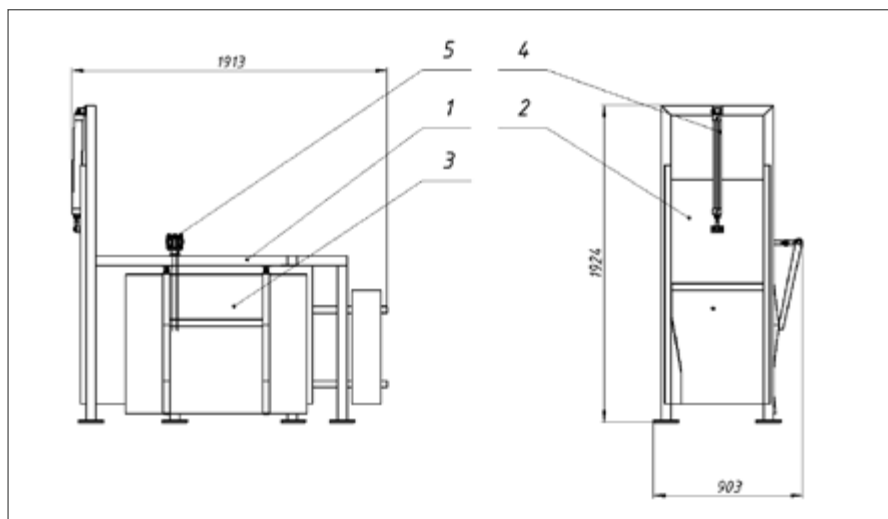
Общий вид бокса: 1 – сварной каркас; 2 – дверь задняя; 3 – дверь боковая; 4 и 5 – пневмоцилиндры
